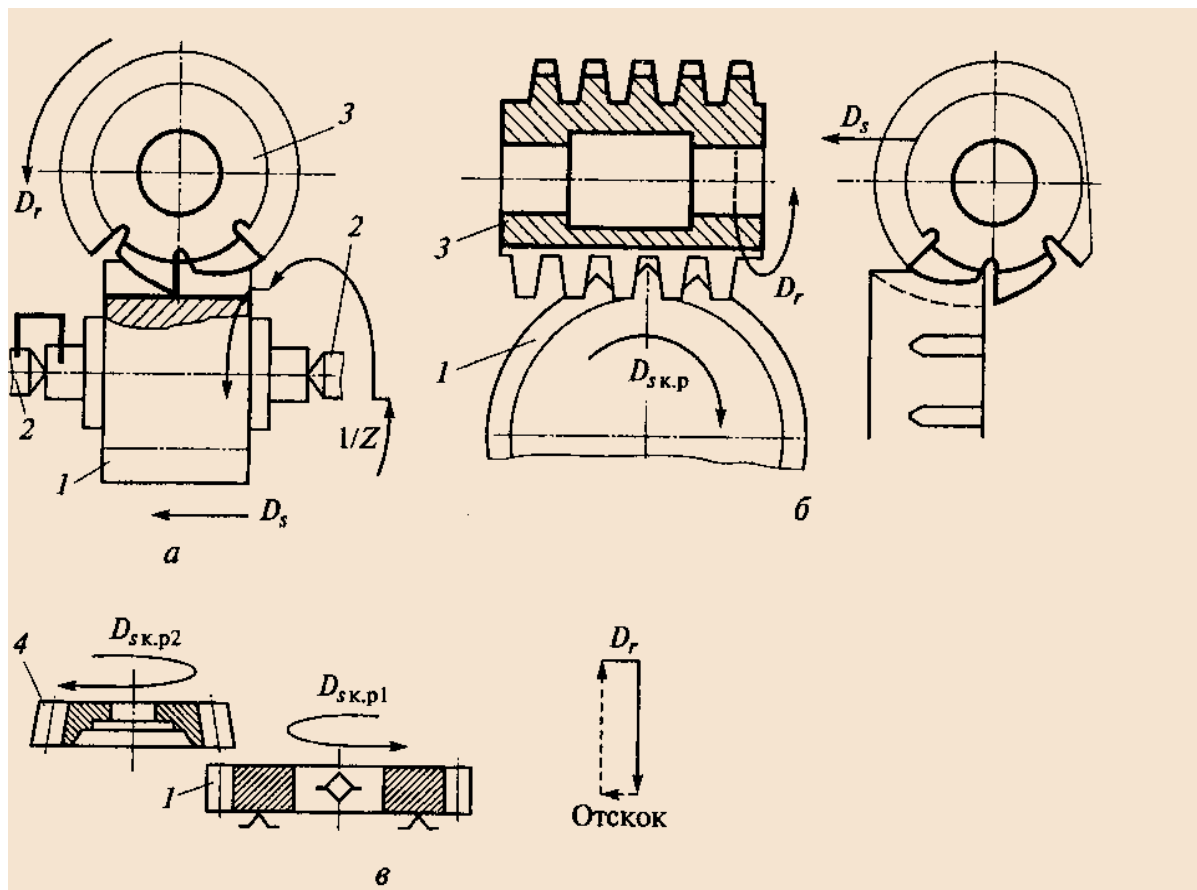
Обработка цилиндрических зубчатых колёс фрезерованием методами копирования (а), обкатки (б) и долбления (в):
